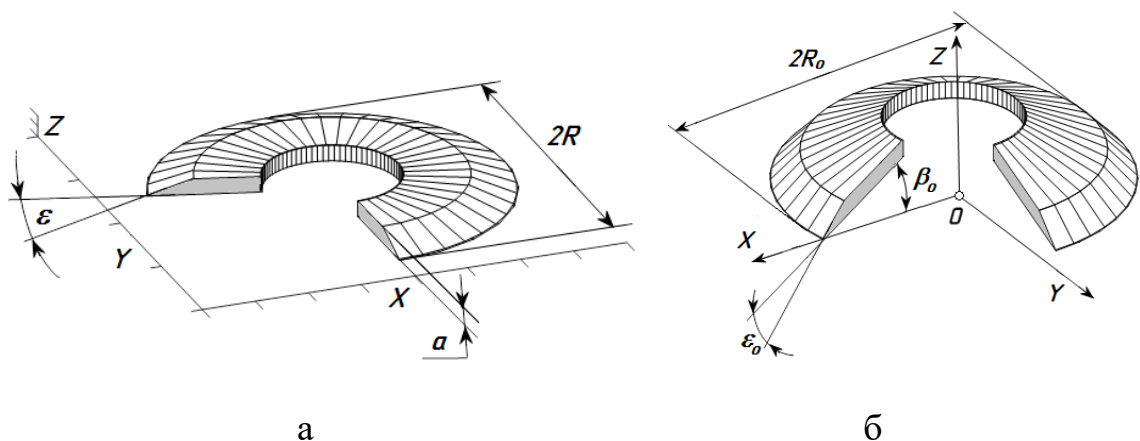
Плоске кільце до і після згинання: а) плоске кільце із знятою фаскою – заготовка для виготовлення диска; б) конічний диск після згинання заготовки (умовно показаний незамкненим)
